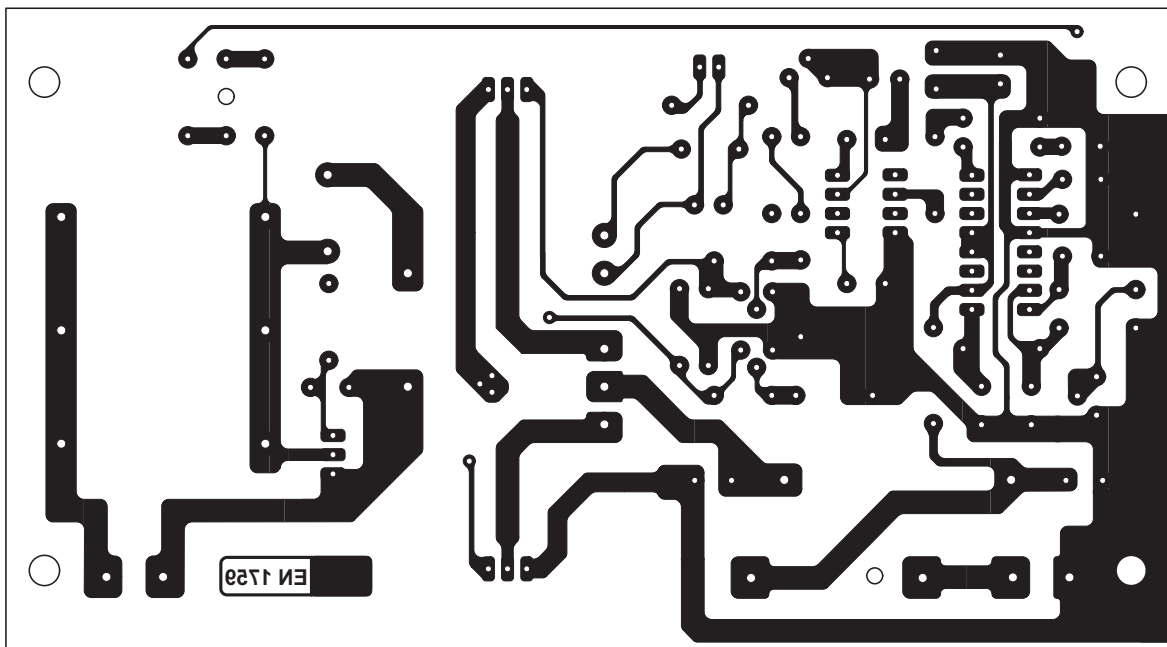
1 : Dessin, à l'échelle 1, du circuit imprimé double face à trous métallisés du générateur EN1759, côté soudure.
